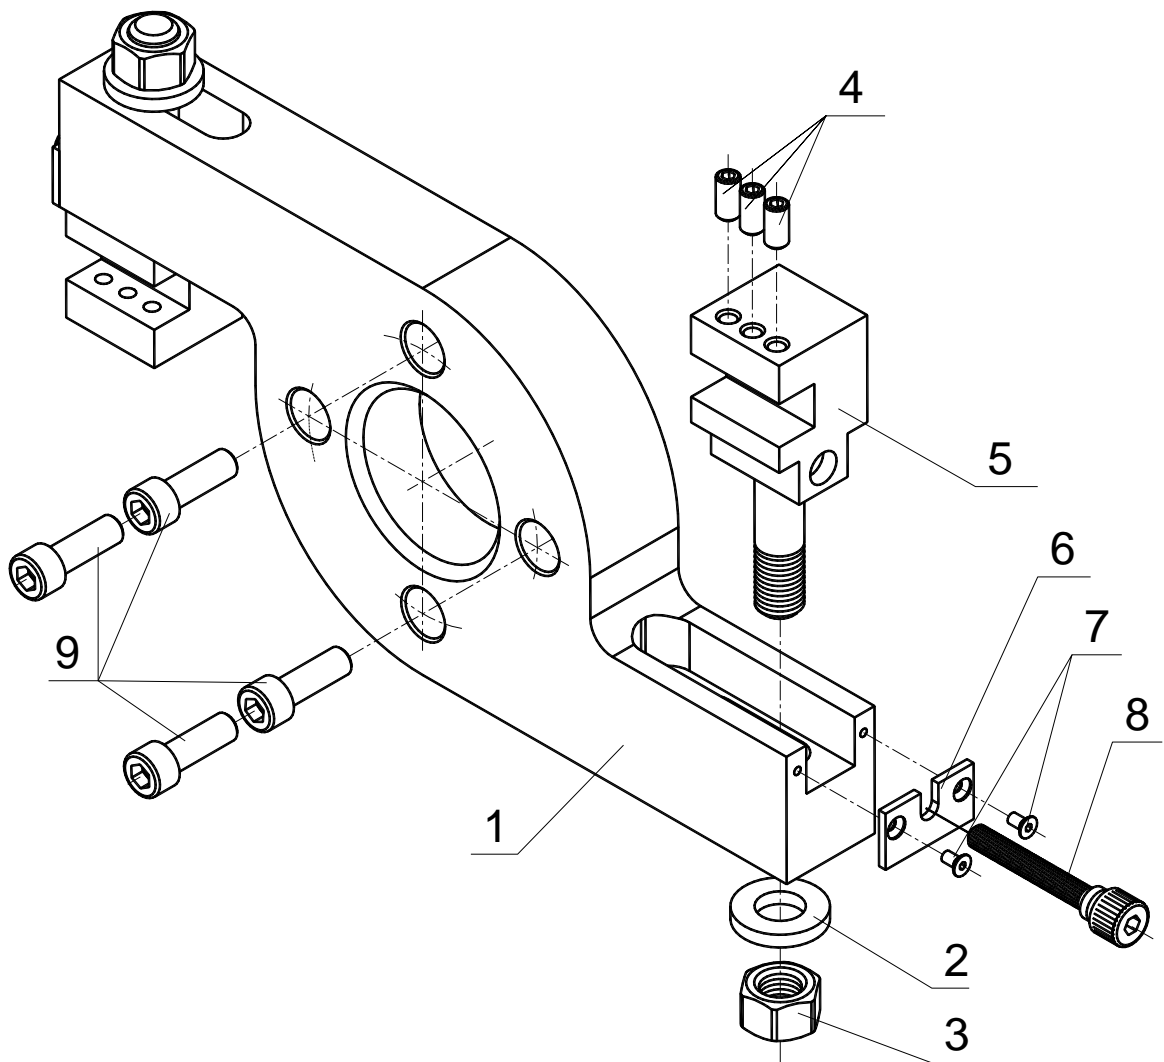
Резцедержатель в сборе М325.60.03.02.00
